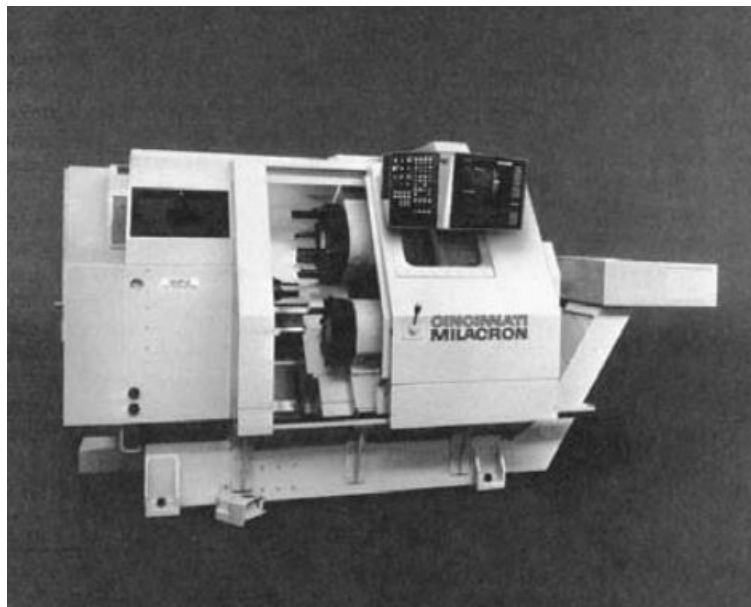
Máquina de torno CNC. (Groover, 2007)
